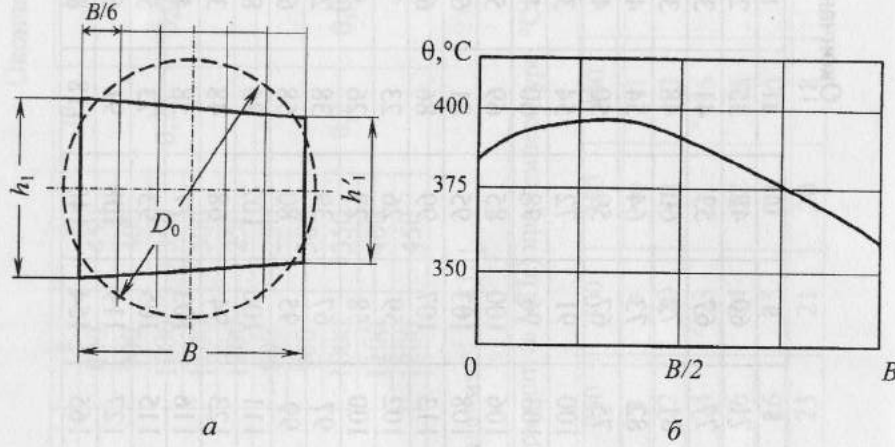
Профиль поперечного сечения заготовки и полосы (а) и распределение температуры по поперечному сечению заготовки (б)
